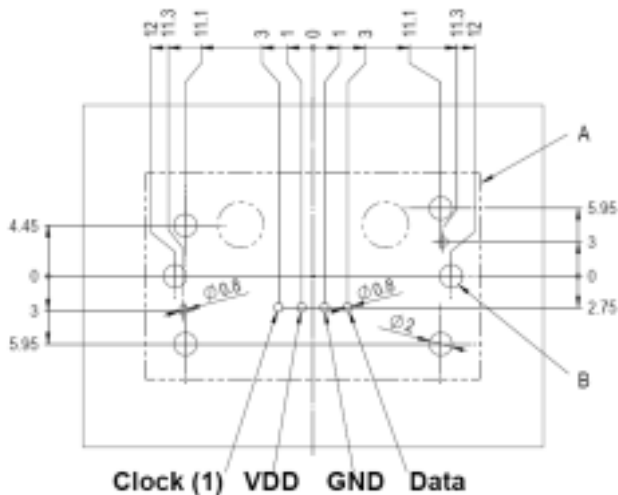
PCB 封装的针脚图。（传感器面的俯视图）。所有尺寸的单位是 mm.
